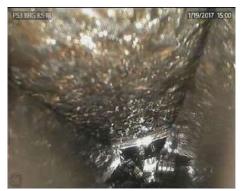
Pista interna e elemento rodante do rolamento – lado do gerador, antes do tratamento
